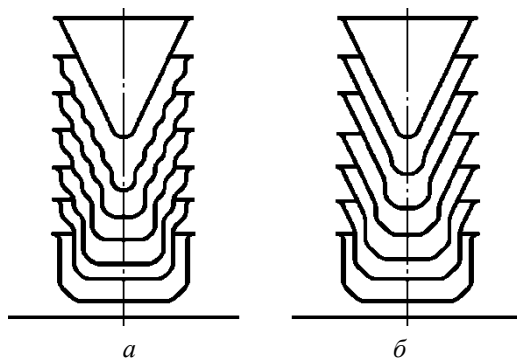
Способы вытяжки конических деталей: *а* – вытяжки ступенчатой детали с последующей калибровкой; *б* – постепенным образованием конуса
